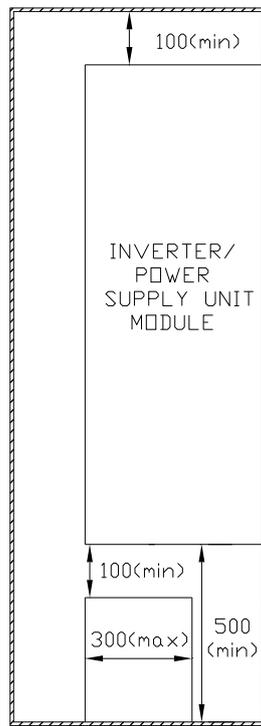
Distanze da mantenere nell'installazione dell'AC/DC UNIT 1050
